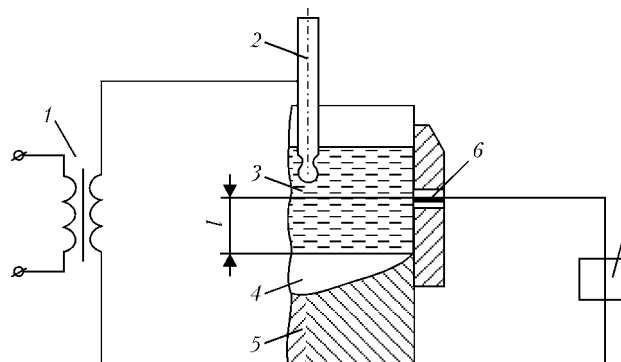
Блок-схема устройства для вывода усадочной раковины: 1 — сварочный трансформатор; 2 — плавающий электрод; 3, 4 — соответственно шлаковая и металлическая ванна; 5 — шов; 6 — щуп; 7 — контролирующий орган
